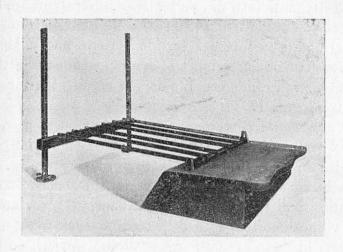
Cavalletto a gambe verticali tipo Spaccamela
